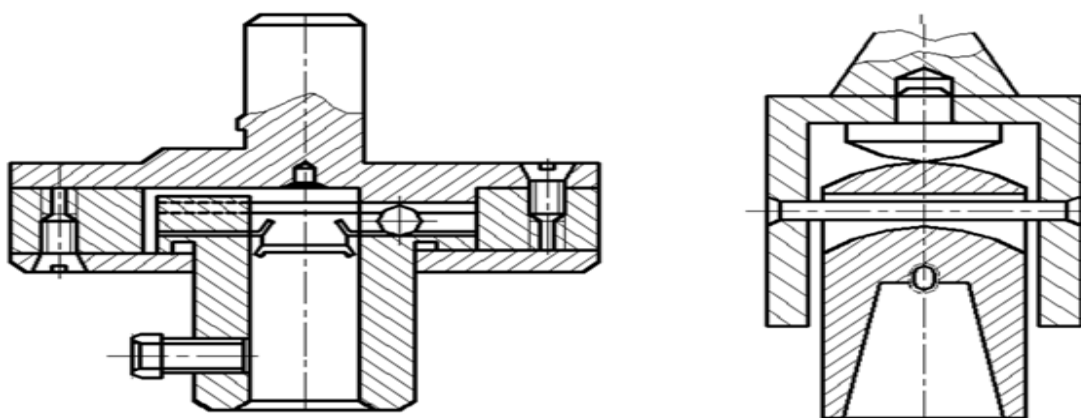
Качающиеся патроны для крепления разверток
